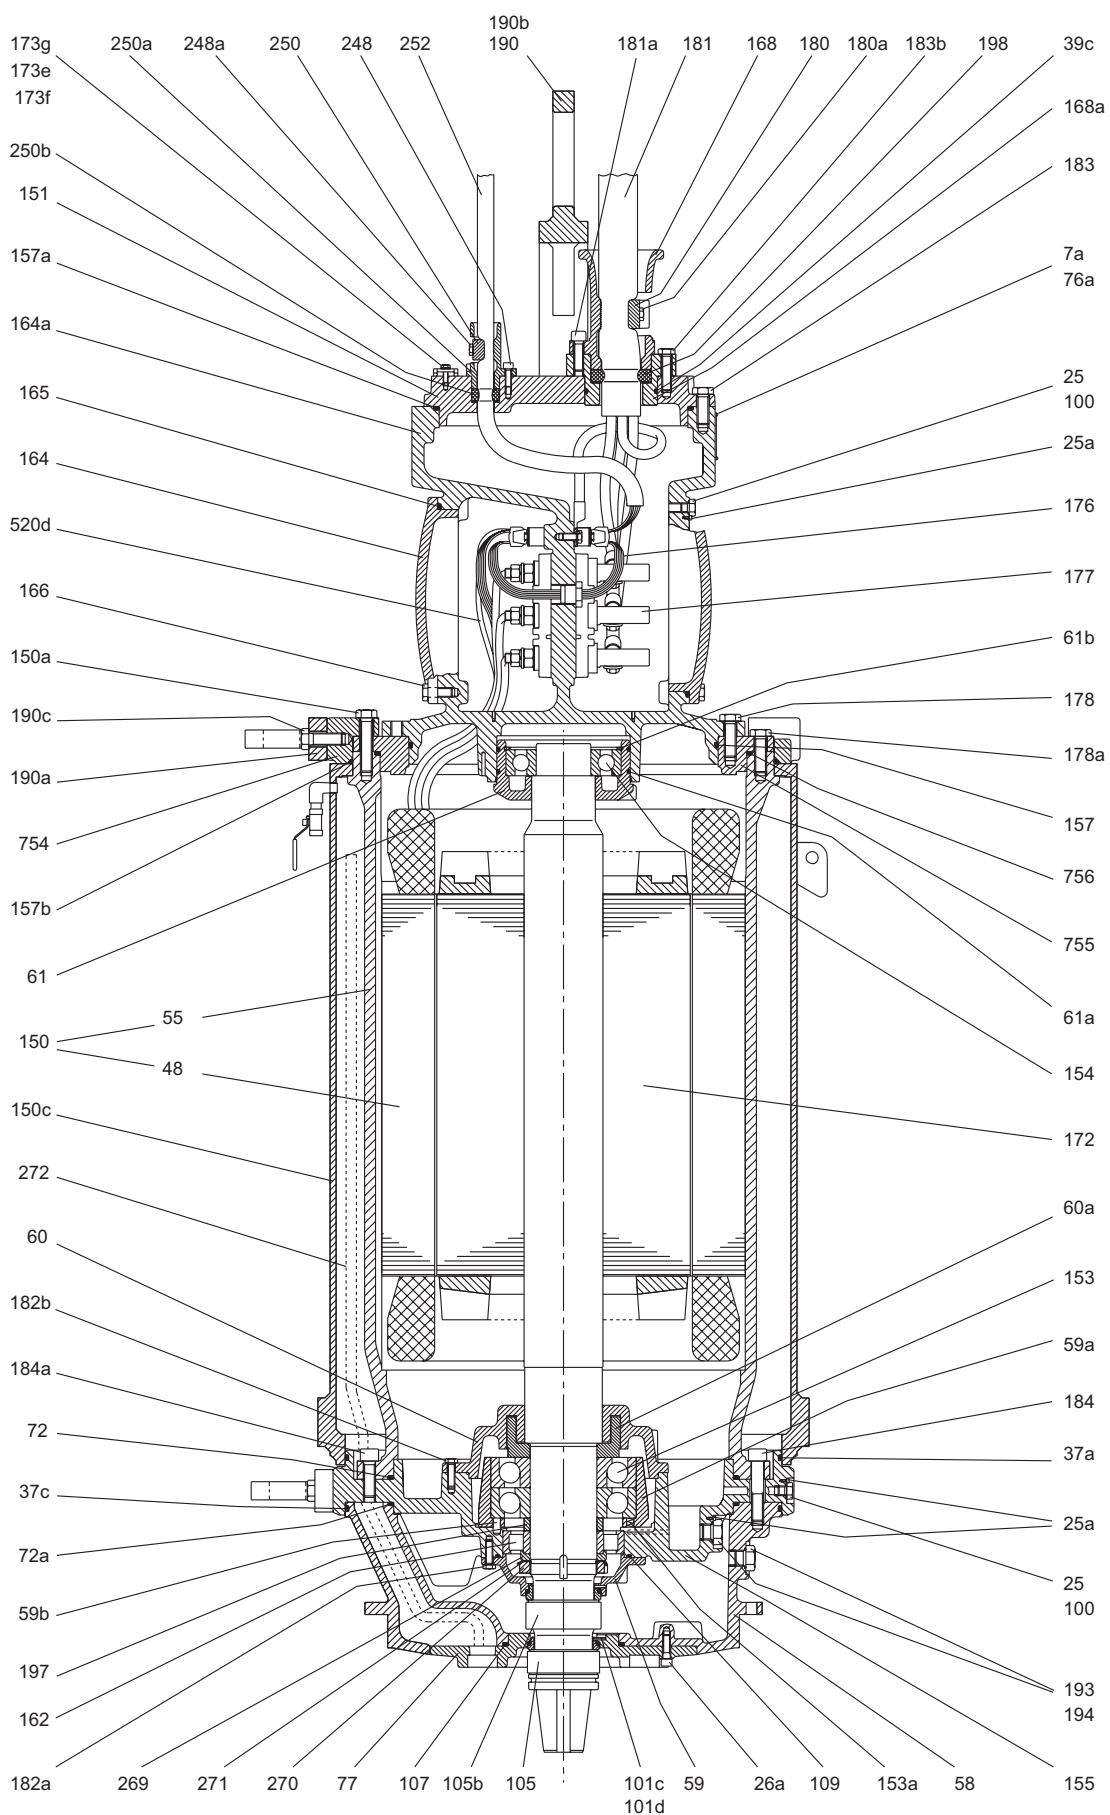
Типоразмер 74, взрывозащищённый двигатель с охлаждающим кожухом.
